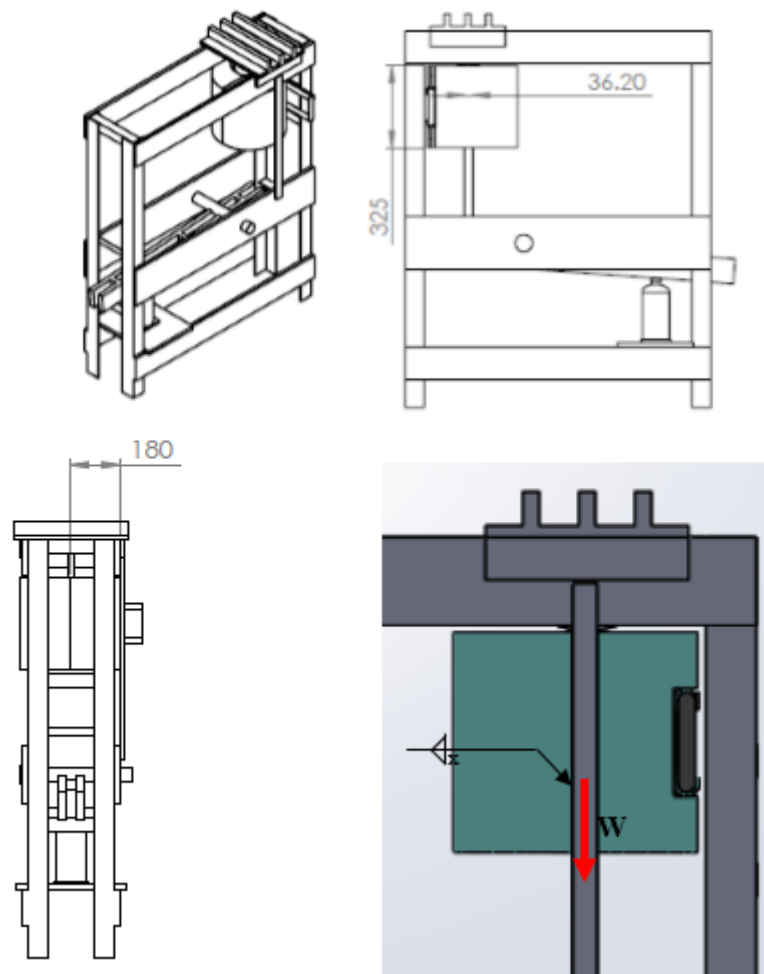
Unión soldada entre el horno y el bastidor
